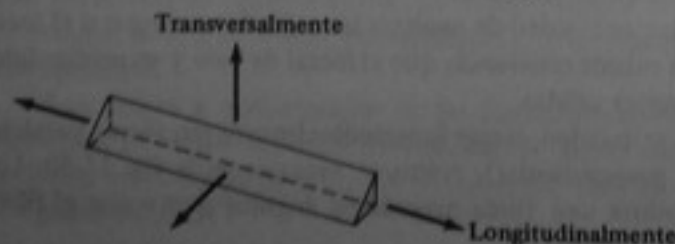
Direcciones de carga para soldadura con filete.
